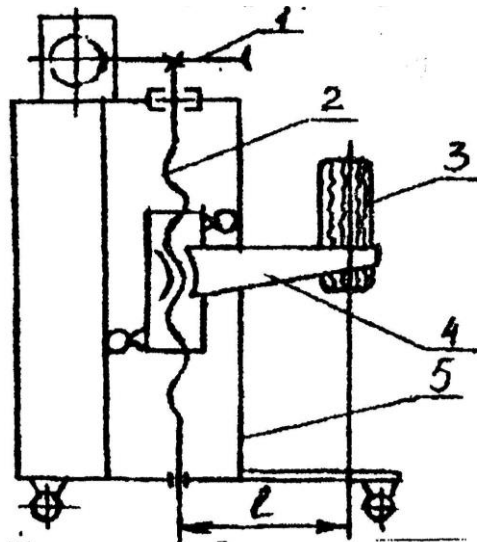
Схема роботи стійки: 1-електромеханічний привод, 2-гвинт; 3-колесо, 4-каретка, 5-стойка
